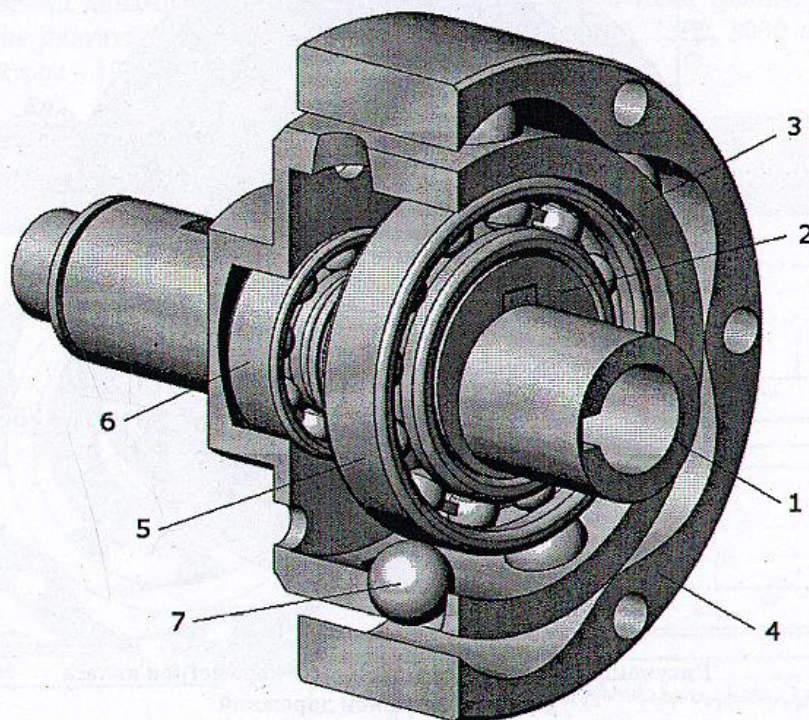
Модель одноступенчатого планетарного радиально-плунжерного редуктора
